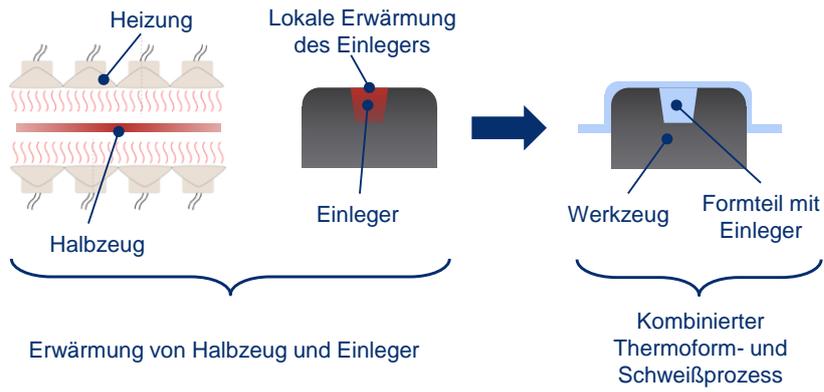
Kombiniertes Thermoform- und Schweißprozess zur Verbindung von Gestaltelementen mit einem thermogeformten Halbzeug
